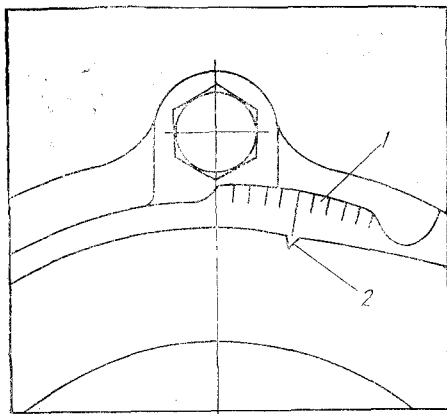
Схема регулювання кута початку подачі палива на двигунах СМД-60, СМД-62:
